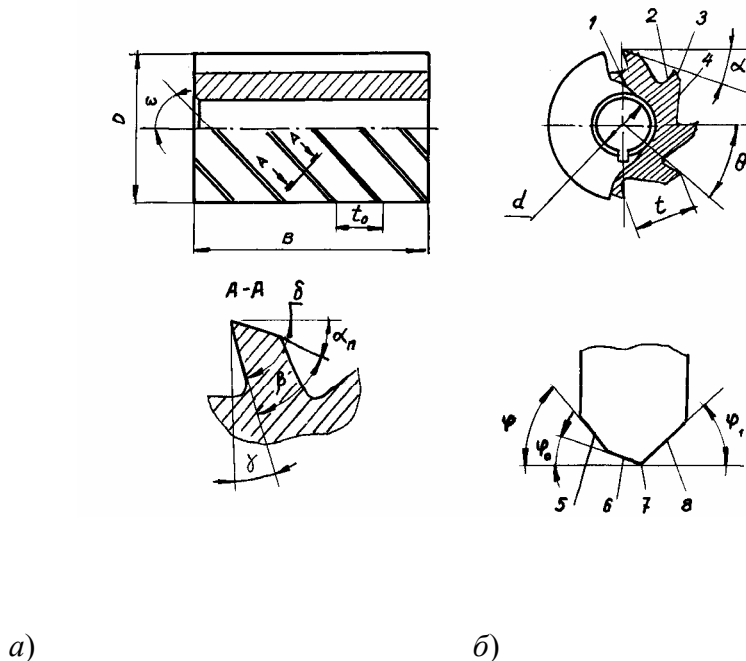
Элементы и геометрия цилиндрической фрезы (а) и геометрия зуба торцевой фрезы (б):
